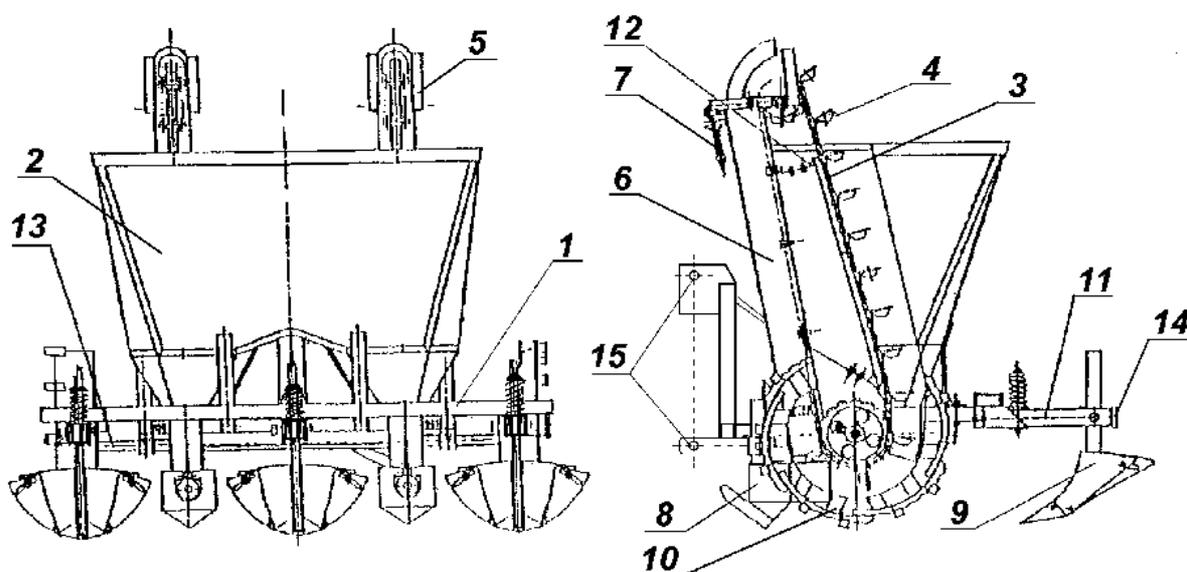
Основные агрегаты переносной автоматической сеялки S239: 1 - рама, 2 - бункер, 3 - цепной транспортер, 4 - черпаки, 5 - головка высаживающего агрегата, 6 - сыпная труба, 7 - натяжное устройство цепи, 8 - дисковый сошник, 9 - заделывающий диск, 10 - ходовое колесо со шпорами, 11 - рычаг заделывающего диска, 12 - агрегат для проведения и встряхивания, 13 - осевой агрегат, 14 - держатели для крепления световых предохраняющих устройств, 15 - система подвески
